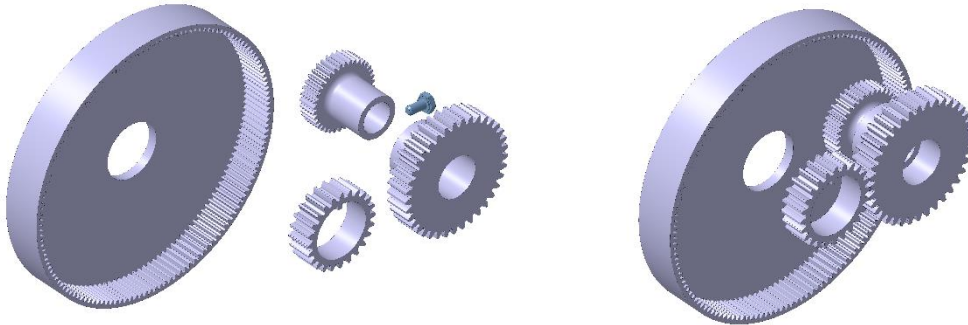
a la izquierda: vista explosionada del sistema de engranajes. A la derecha: vista isométrica del tren de engranajes ensamblado.
